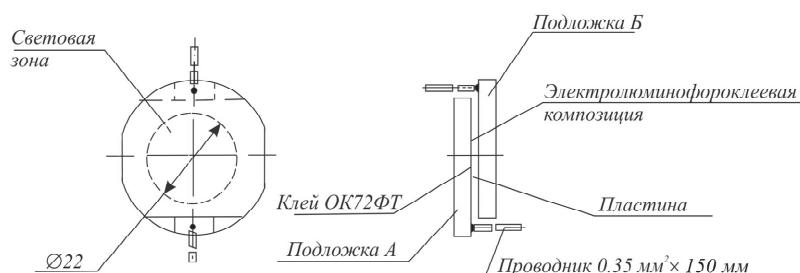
Конструктивный эскиз собранного преобразователя изображений
